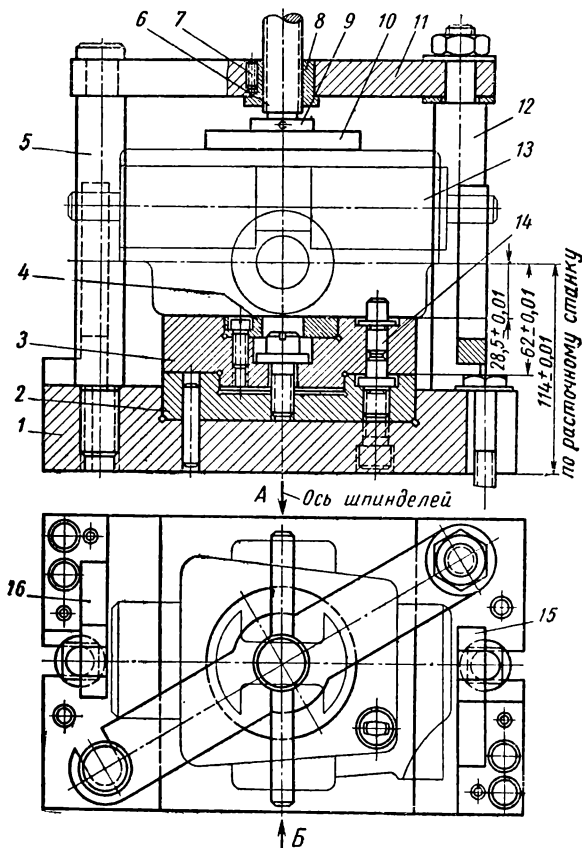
Приспособление для установки детали на алмазно-расточном станке
